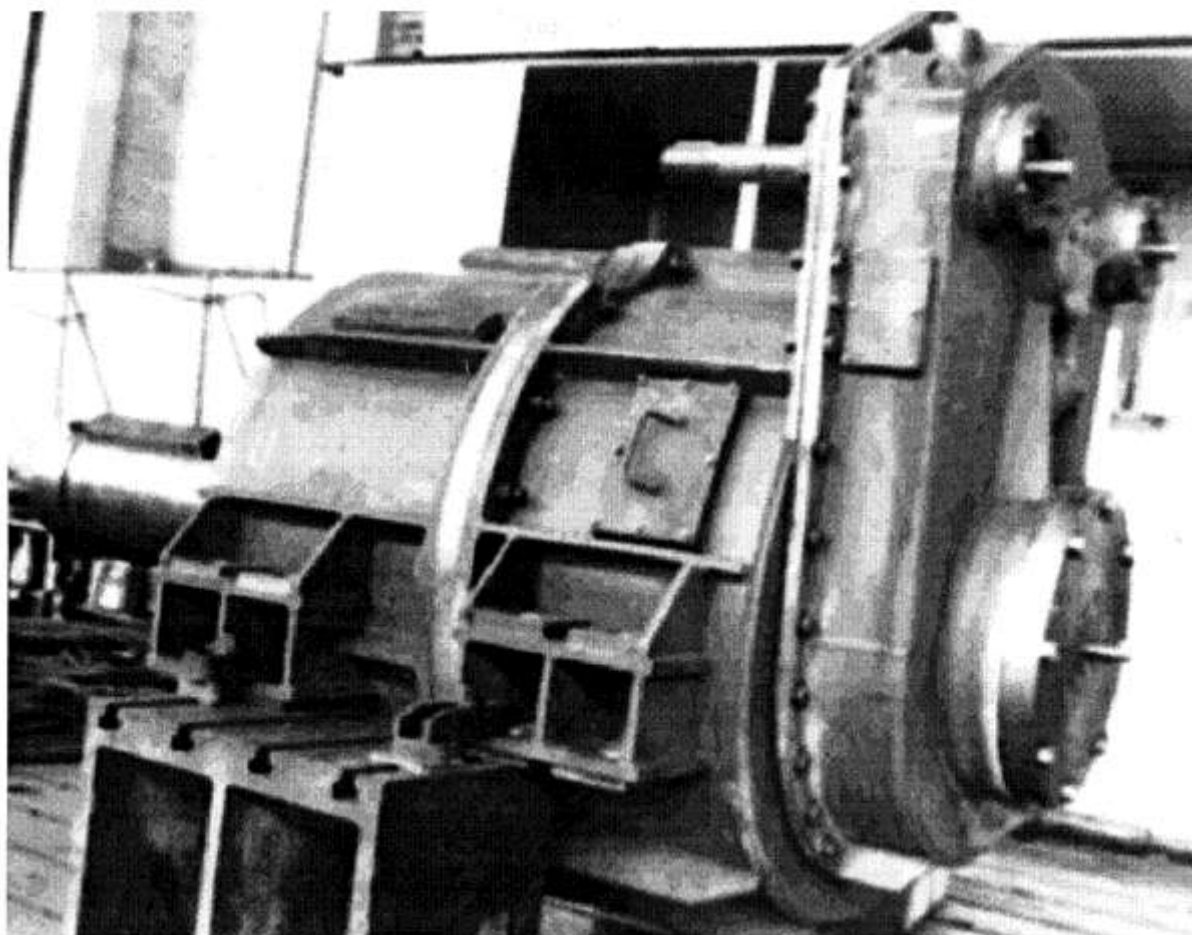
Волновой зубчатый редуктор ВЗ – 1120 поворота иксеры МП–600АС
